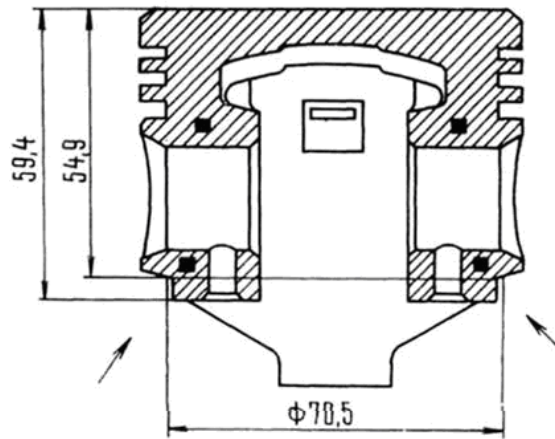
Схема удаления металла с поршня для подгонки его веса.
